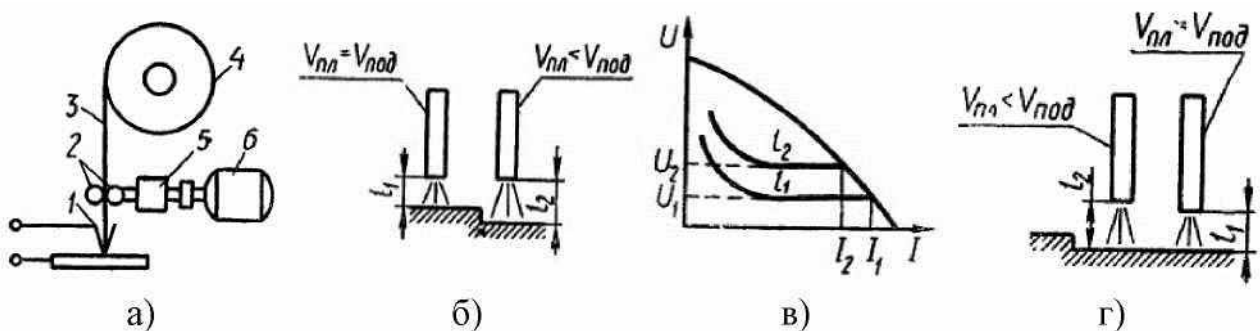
Схеми пристрою зварювального автомата та пресу саморегулювання довжини дуги
